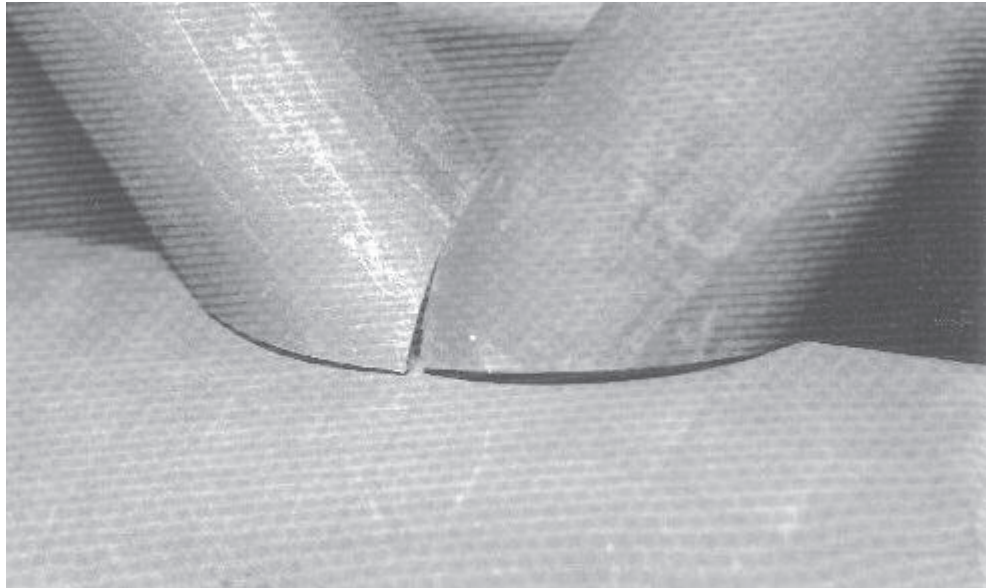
Nudo fabricado por aserrado de corte plano antes de soldar.
